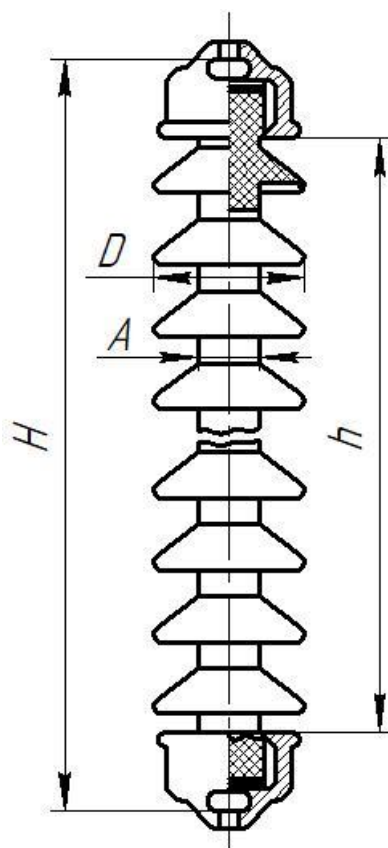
Конструкція опорного ізолятора ОНБ зовнішньої установки
